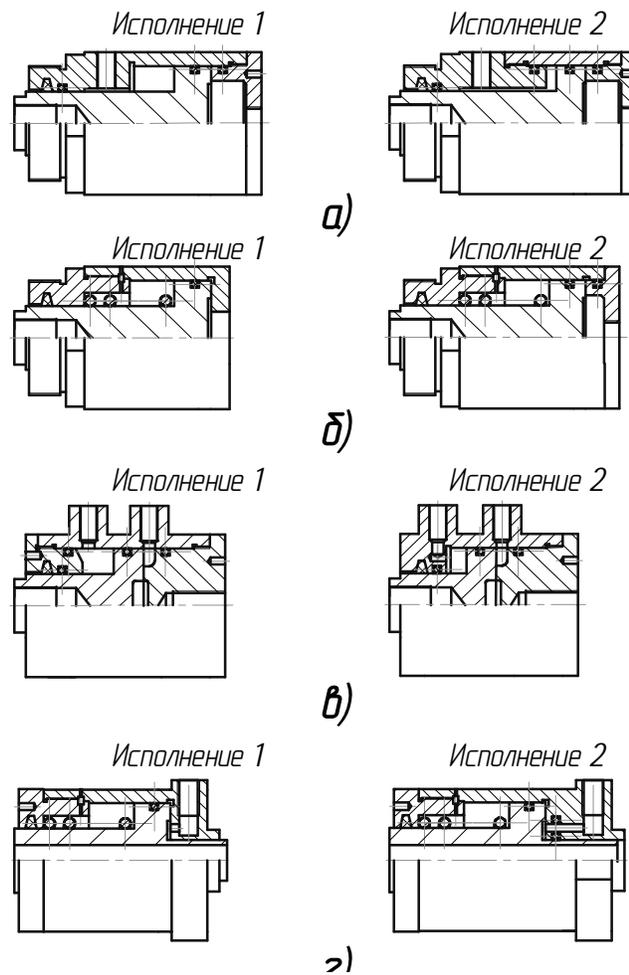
Гидроцилиндры (а – двухсторонние, с креплением по наружной резьбе; б – односторонние, с креплением по наружной резьбе; в – двухсторонние, с креплением по резьбовому отверстию; г – односторонние, с полым штоком)
